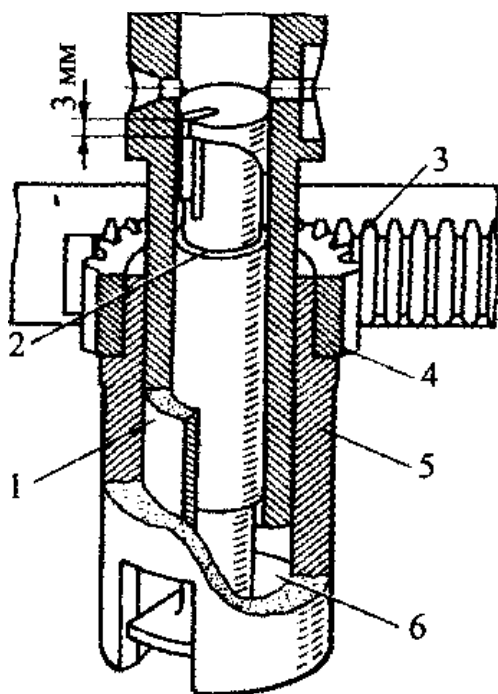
Механізм повороту плунжера золотникового ПНВТ:
